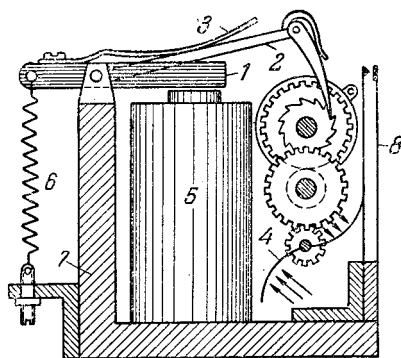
Схема реле с часовым механизмом и воздушным демпфером: 1—якорь; 2—рычаг; 3—плоская пружина; 4—лопасти; 5—катушка электромагнита; 6—оттяжная пружина; 7—ярмо электромагнита; 8—контактные пластины, замыкаемые выступом (кулачком) верхнего колеса.
